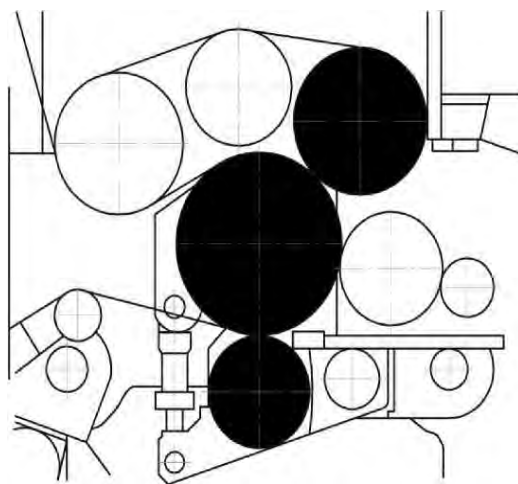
Схема гофропресса с прижимным сукном вместо прижимного вала
